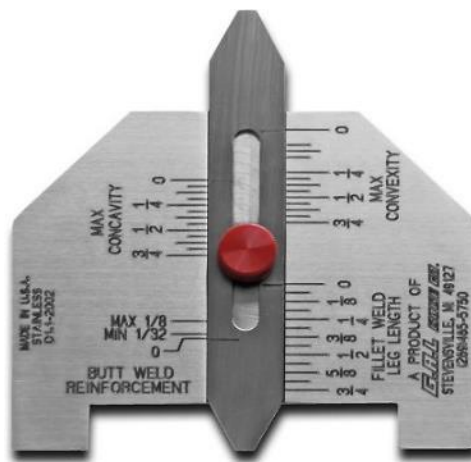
Galgas de soldadura de filete fijas [7]
